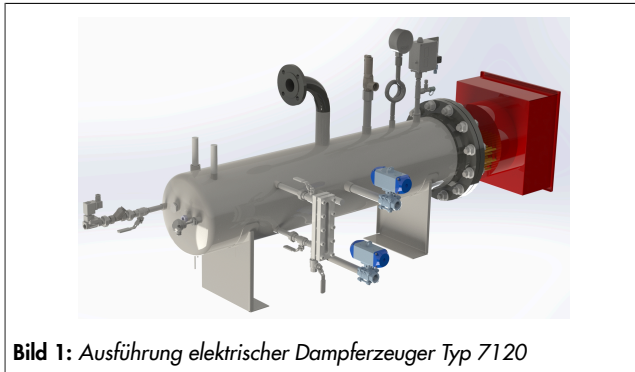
Ausführung elektrischer Dampferzeuger Typ 7120
